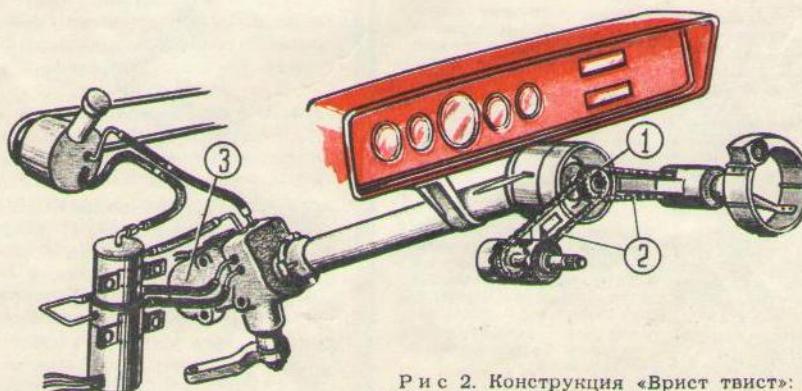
Конструкция «Врист твист»: 1 — муфта рулевой колонки; 2 — цепная передача; 3 — сервомеханизм.
